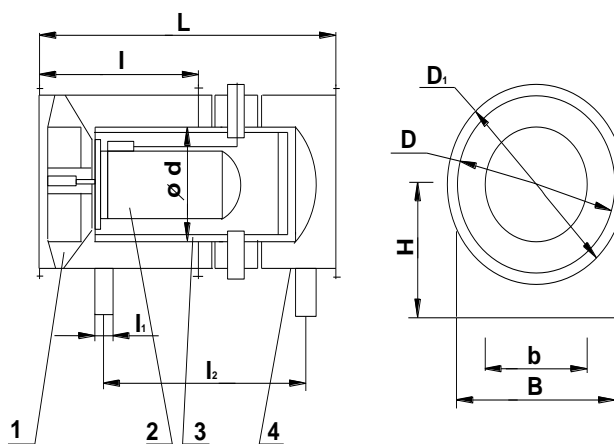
Габаритные, присоединительные и установочные размеры, вентилятора осевого типа
